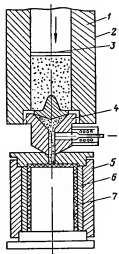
Схема установки для нанесения покрытия из расплава полимеров методом литья под давлением: 1 — рабочий цилиндр; 2 — нагреватель; 3 — плунжер; 4 — сопло запорного крана; 5 — пресс-форма; 6 — деталь; 7 — напыленный слой
